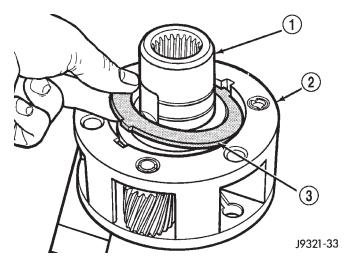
Desmontaje del retenedor de engranaje impulsor
